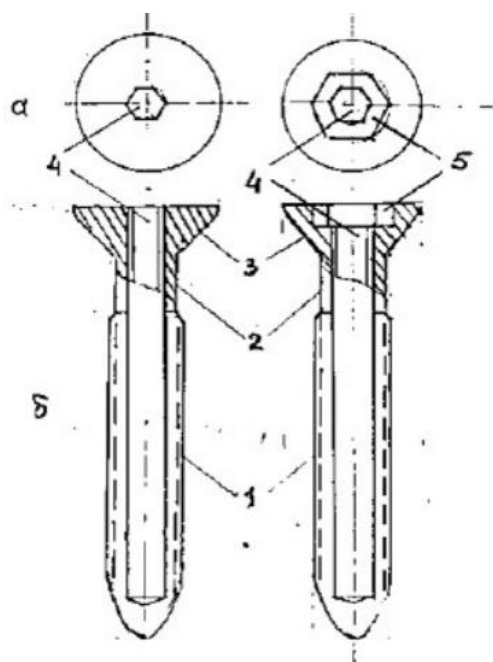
Эскиз костного шурупа (а- вид сверху; б- вид с боку): 1- резьбовая часть; 2- шейка; 3- головка; 4- не сквозное четырех- или шестигранное отверстие под ключ на длину винта; 5- дополнительное внутреннее отверстие под ключ в головке шурупа
